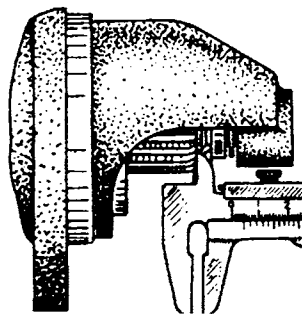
Замер зазора от торца шестерни до упорного кольца
